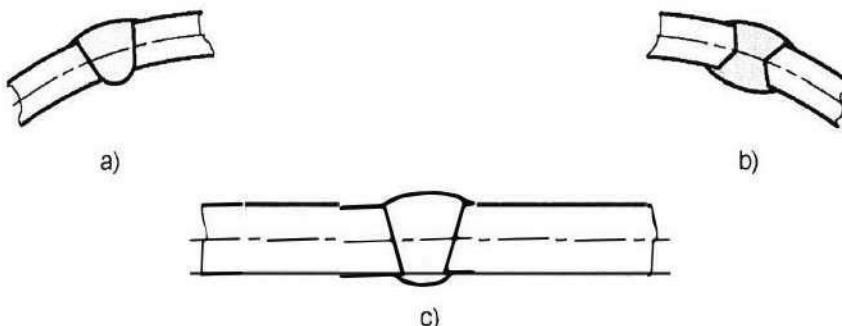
Примеры типовых стыковых соединений пластин равной толщины
